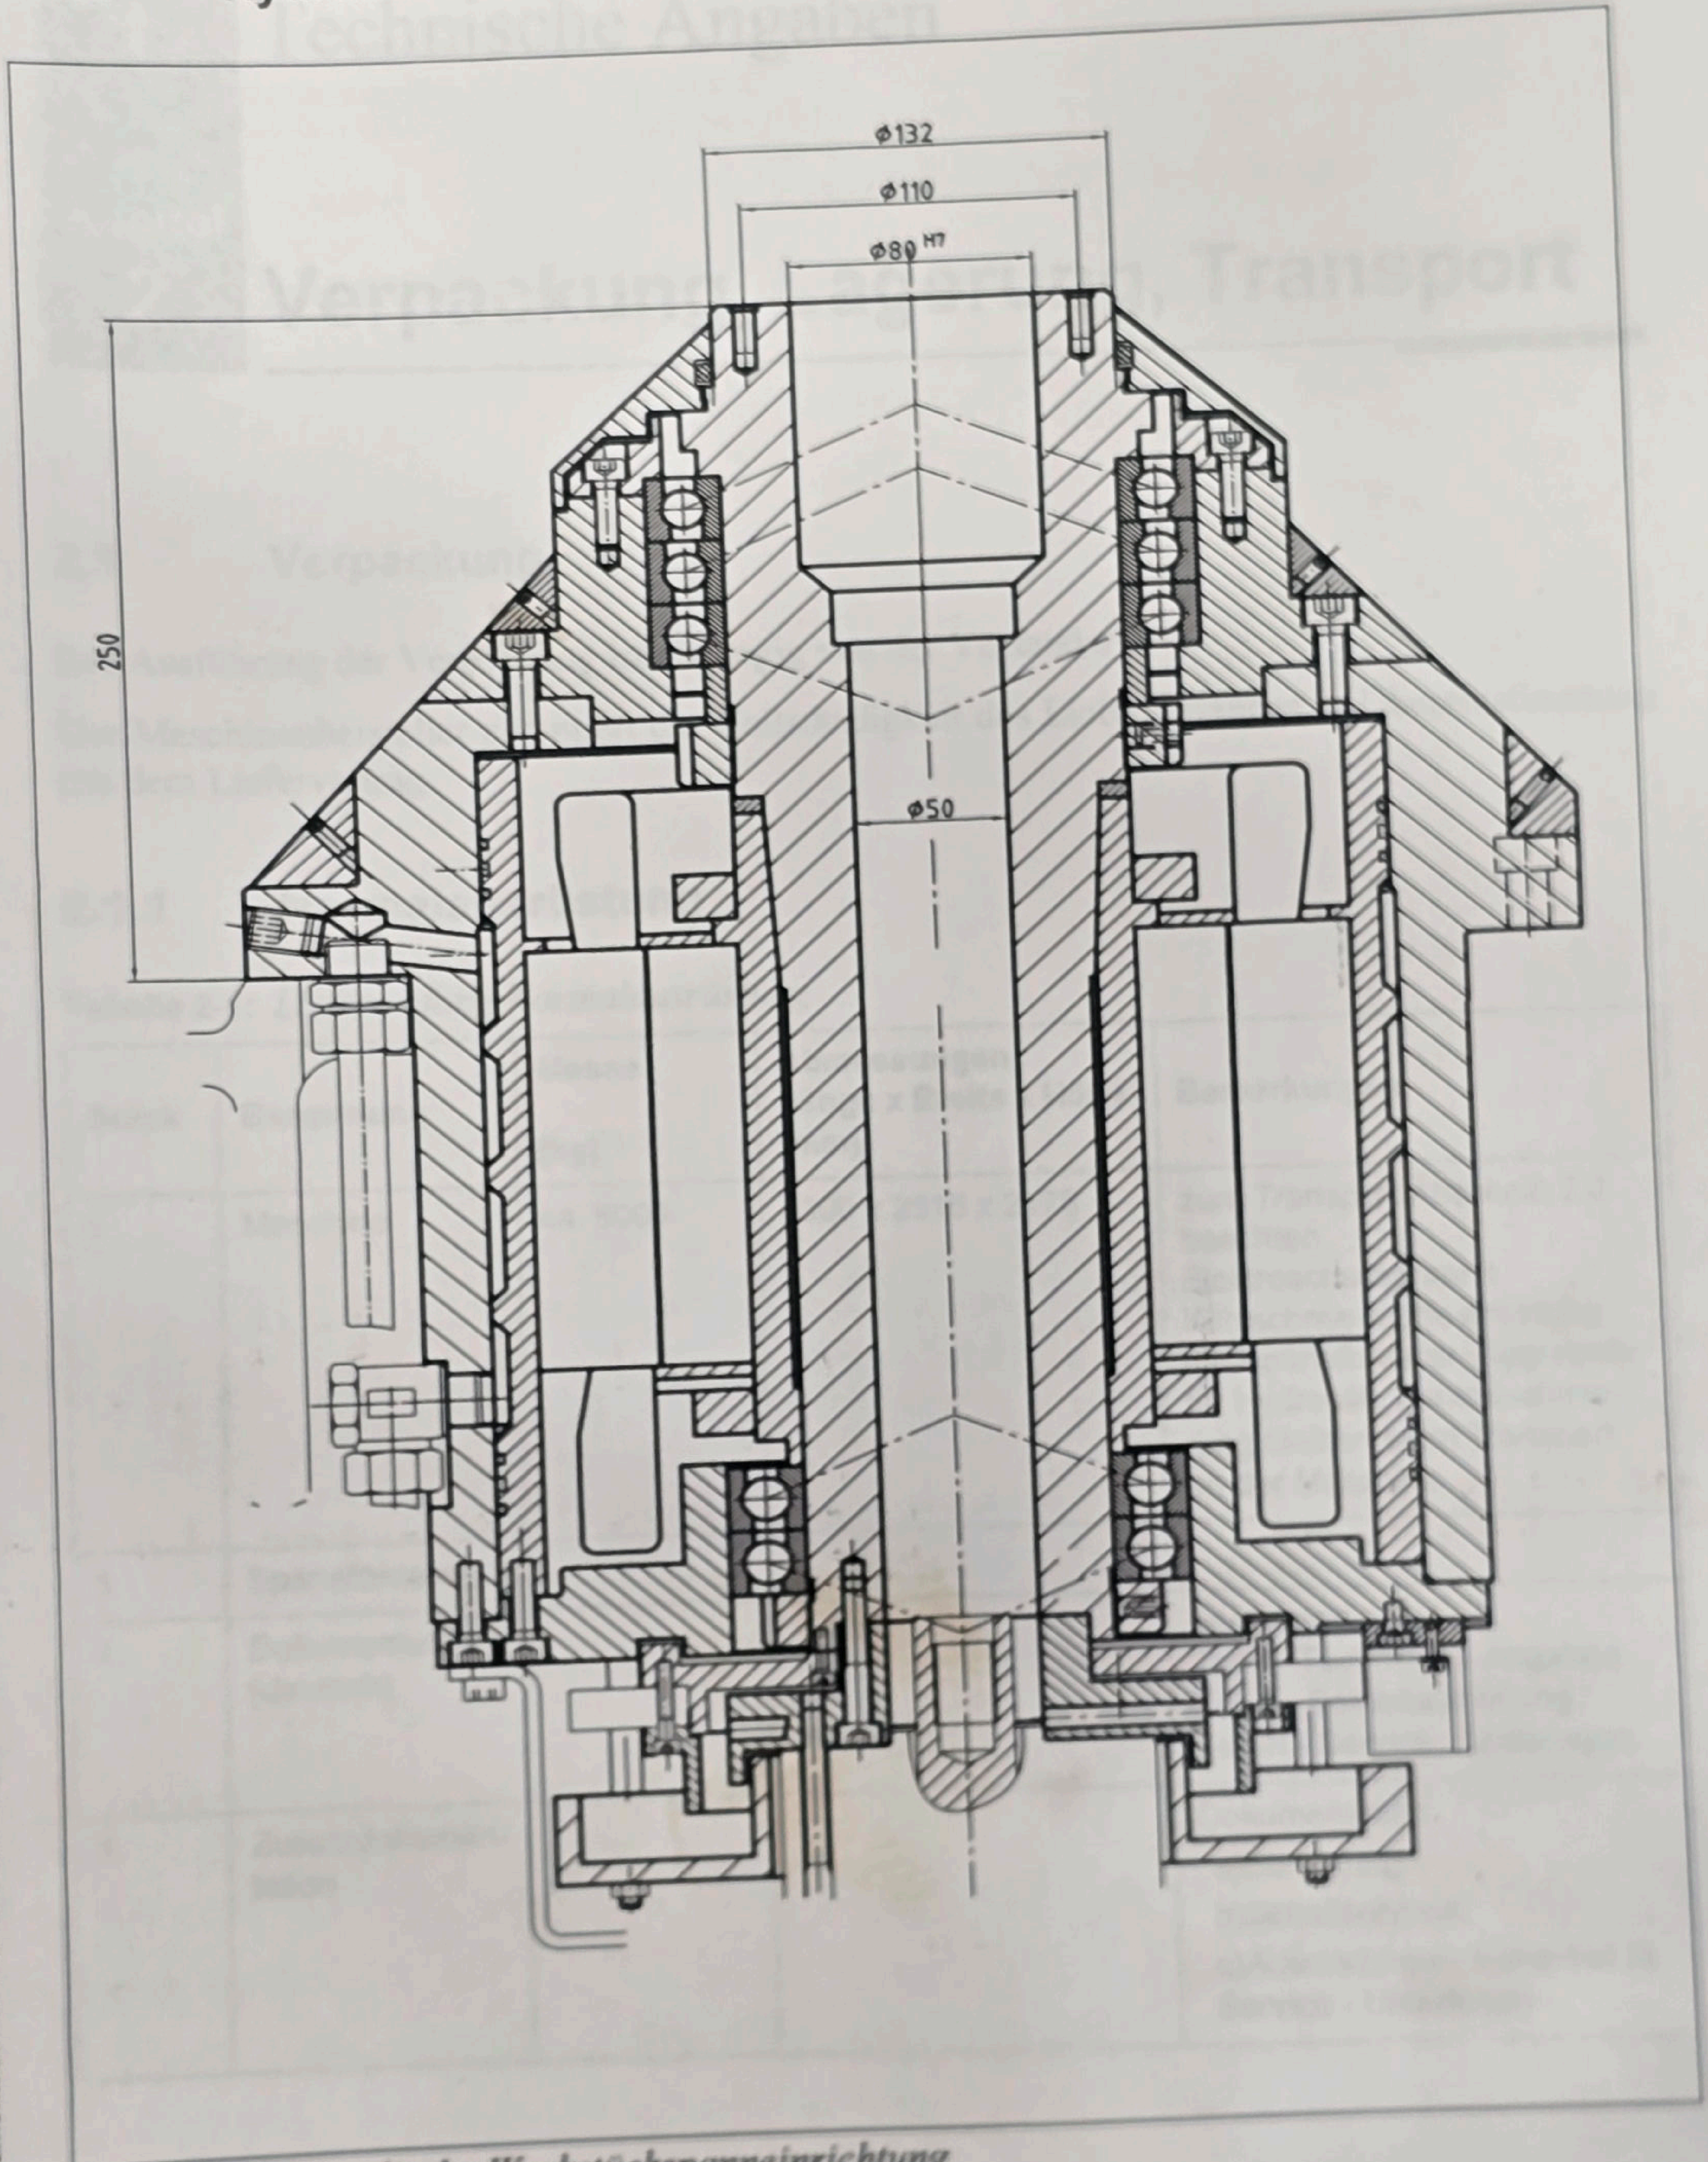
Hydraulische Werkstückspanneinrichtung
